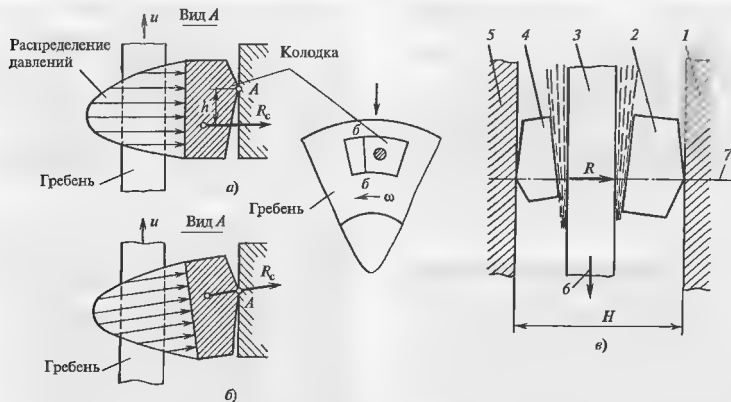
Положение колодок и гребня в упорном подшипнике
